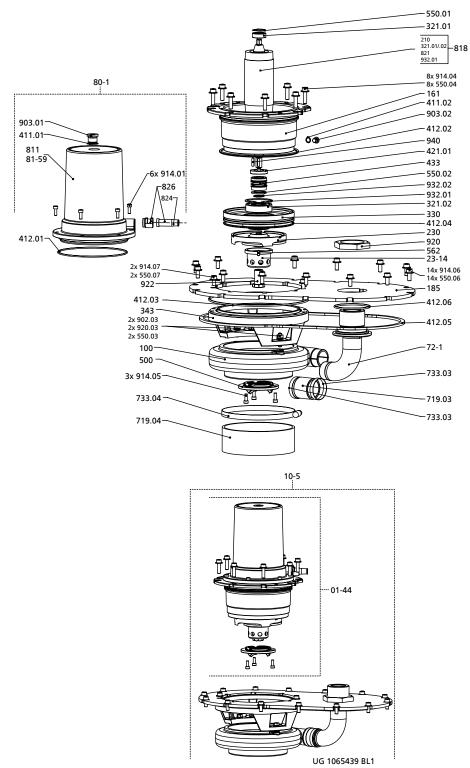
Деталировочный чертеж US100, UZS150 - ходовая часть
